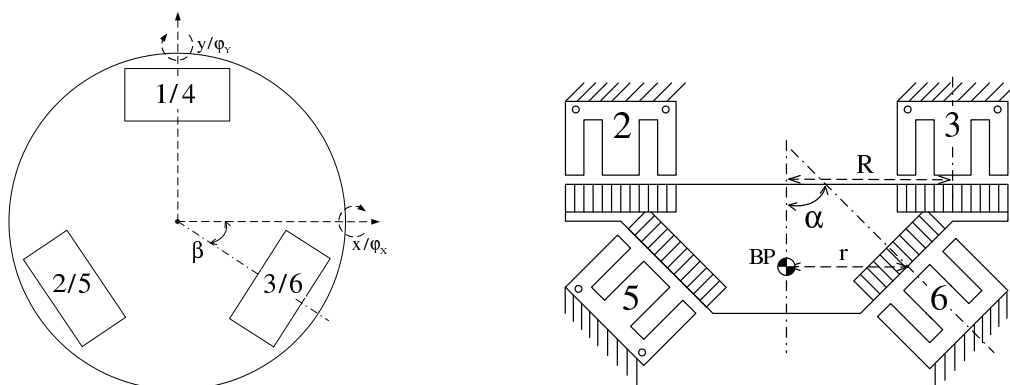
Draufsicht und Seitenansicht auf die vereinfachte Magnetanordnung des „Prototyps-3“
